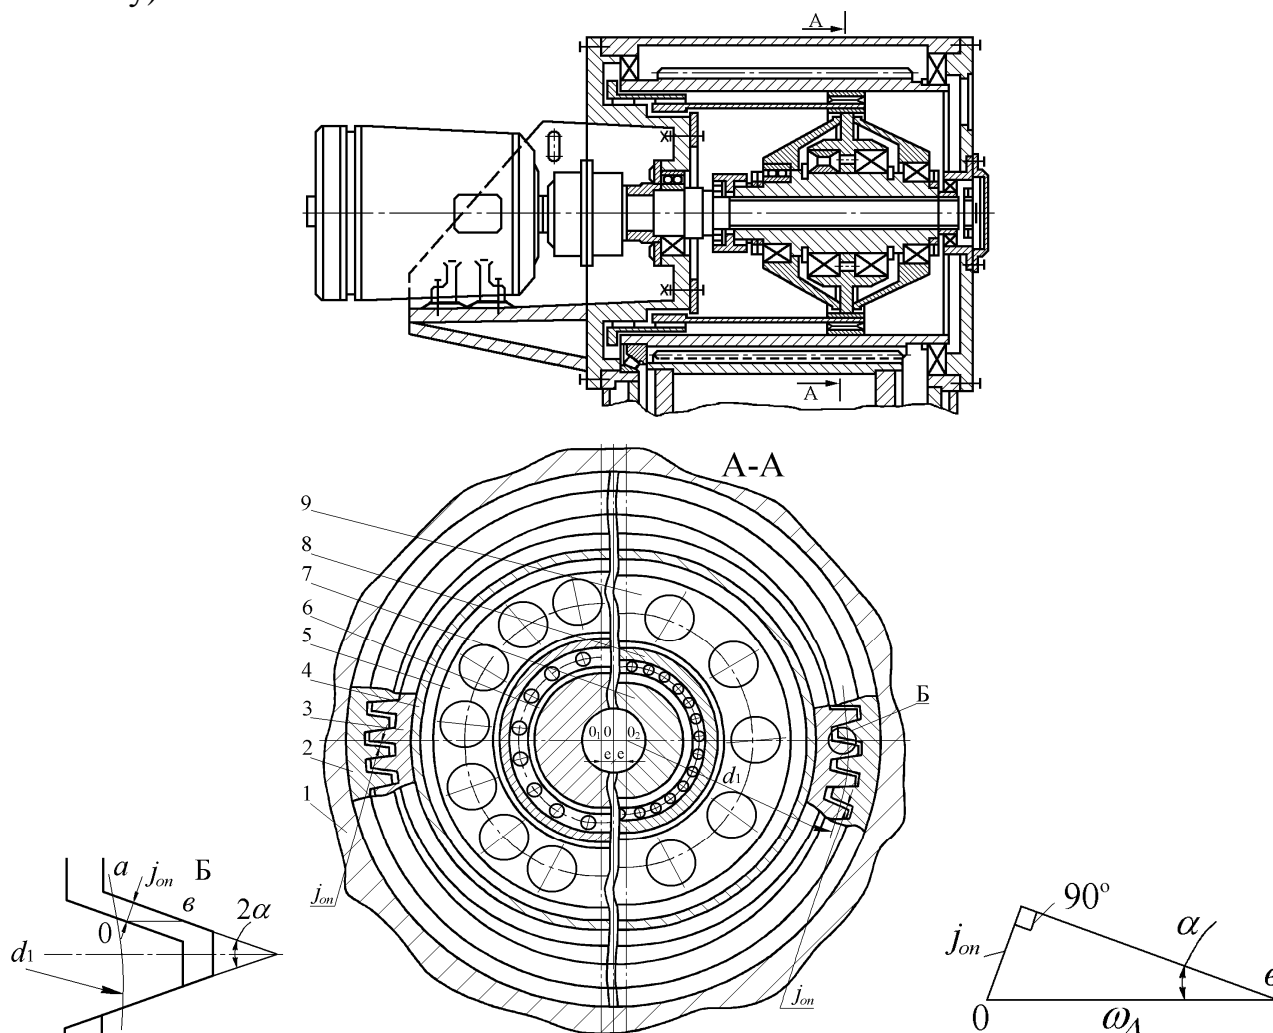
Поперечний розріз хвильової зубчастої передачі в площині генератора привода конвертора: 1 - корпус; 2 - жорстке колесо; 3 - гнучке колесо; 4 - проставочне колесо; 5 - диск середній; 6 - підшипник; 7 - вал ексцентриковий; 8 - підшипник; 9 - диск крайній
